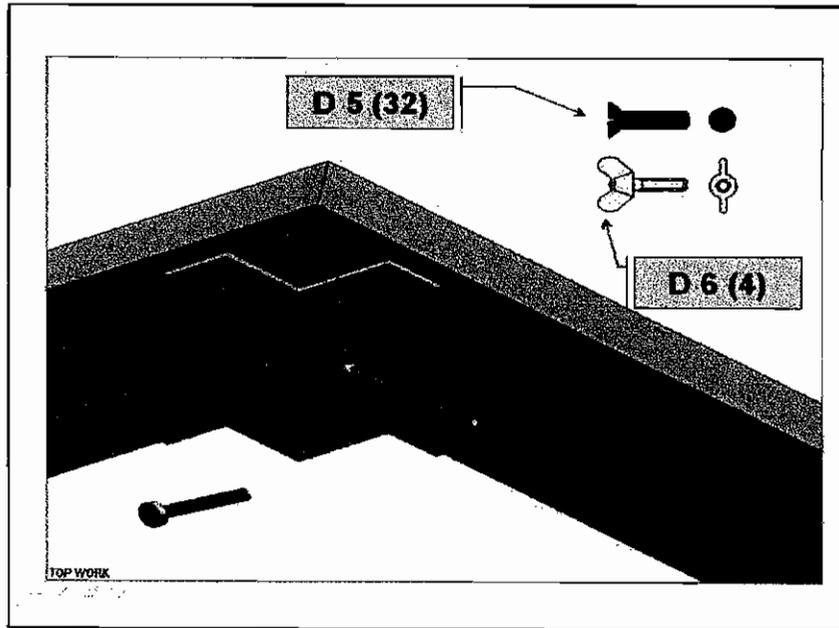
Assembly drawing ของโต๊ะพับแบบถอดประกอบได้ (2)
